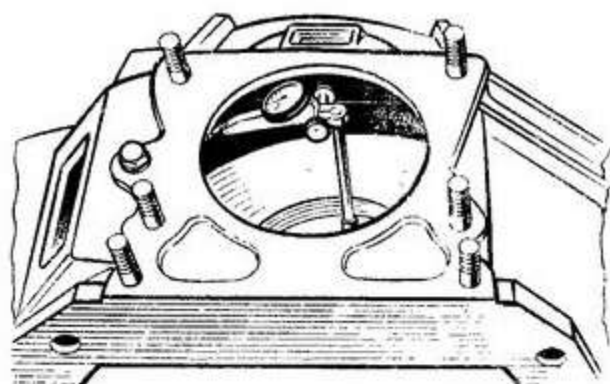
Проверка concentricity установочного отверстия в картере сцепления с осью коленчатого вала
